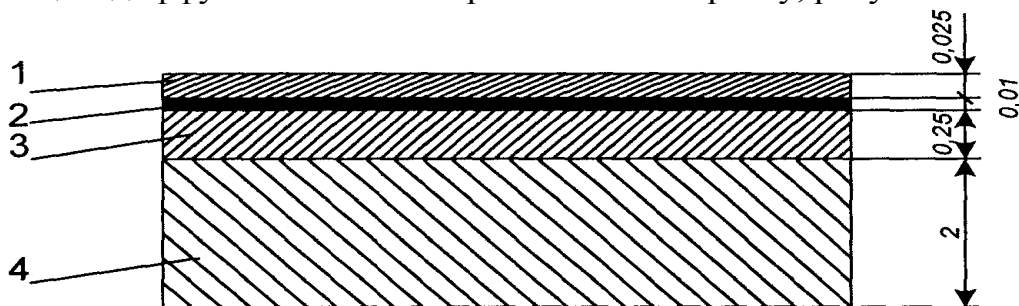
Схема строения четырехслойного металлического подшипника скольжения: 1 – сплав свинца и олова; 2 – никель; 3 – свинцовистая бронза; 4 – сталь
